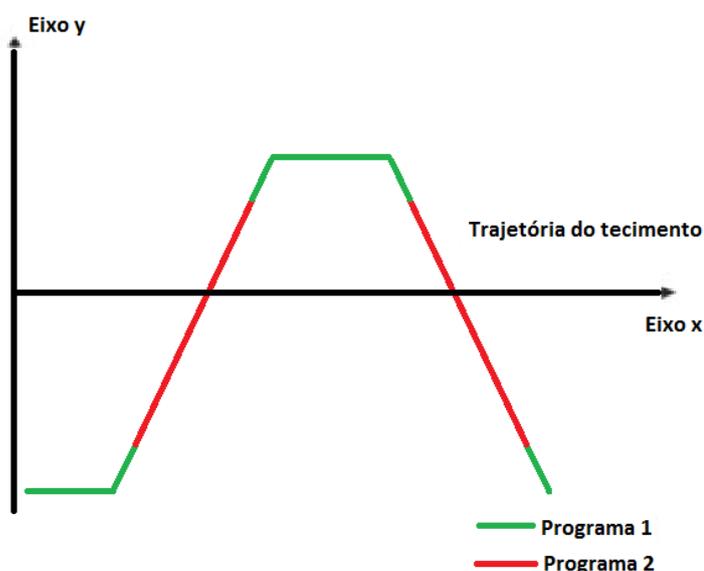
Tecimento - Inclinação no plano vertical
